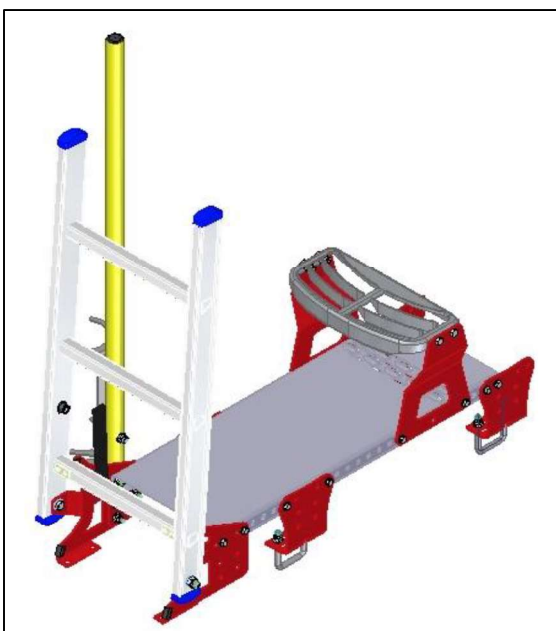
kit de plateforme VS600-1200 sans roues de jauge à l'arrière
